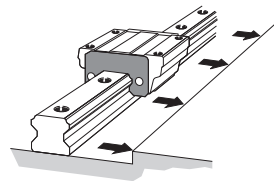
Выравнивание рельса LM относительно базовой поверхности
